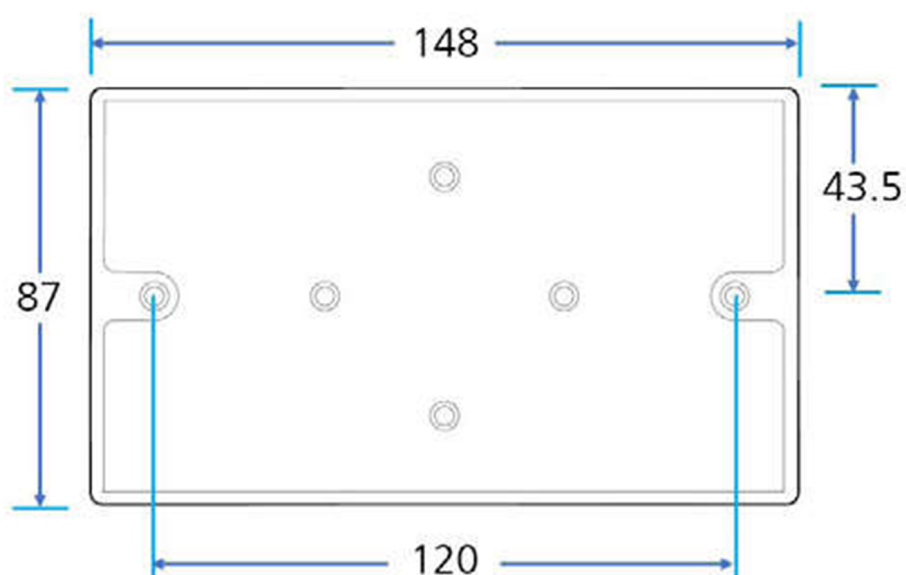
Dimensiones de la caja trasera de montaje en superficie
